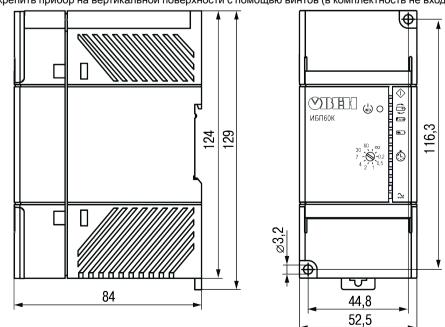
Внешний вид, габаритные и установочные размеры прибора
